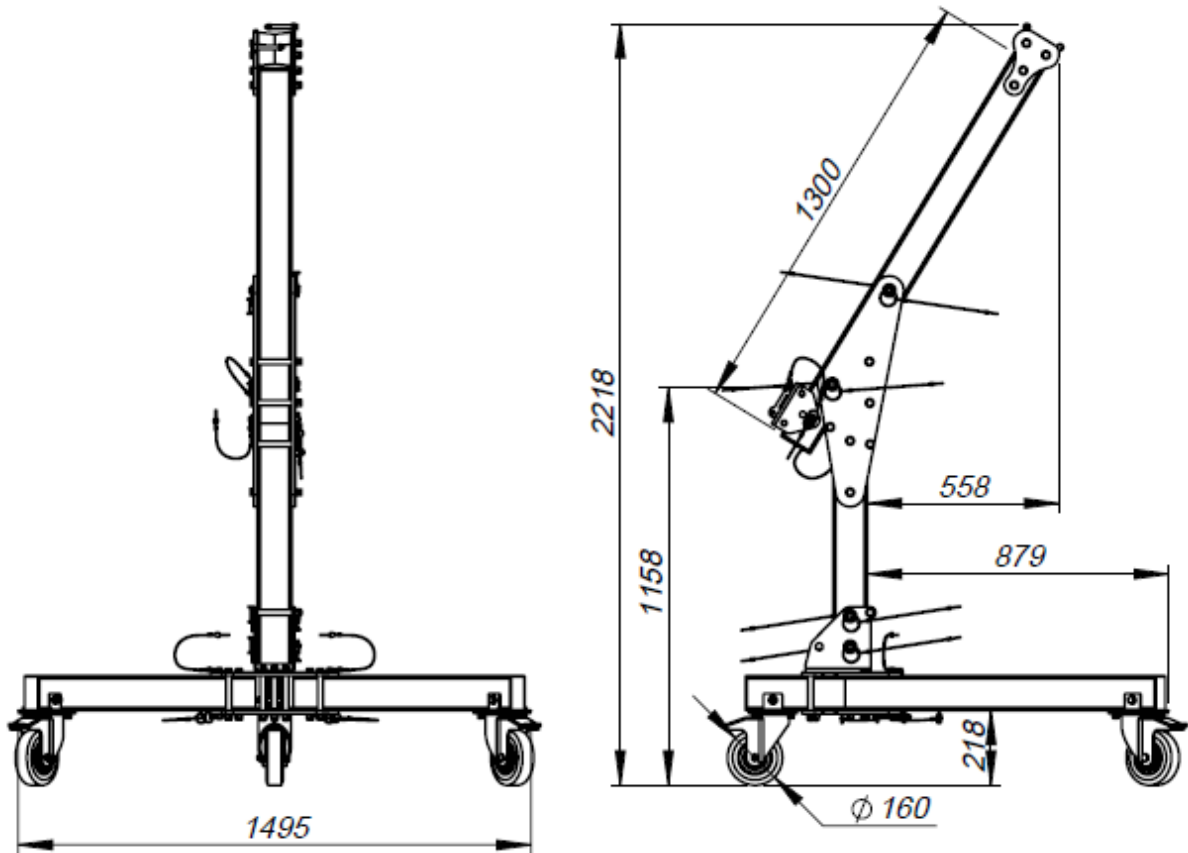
Dimensiones generales del dispositivo - vista frontal
